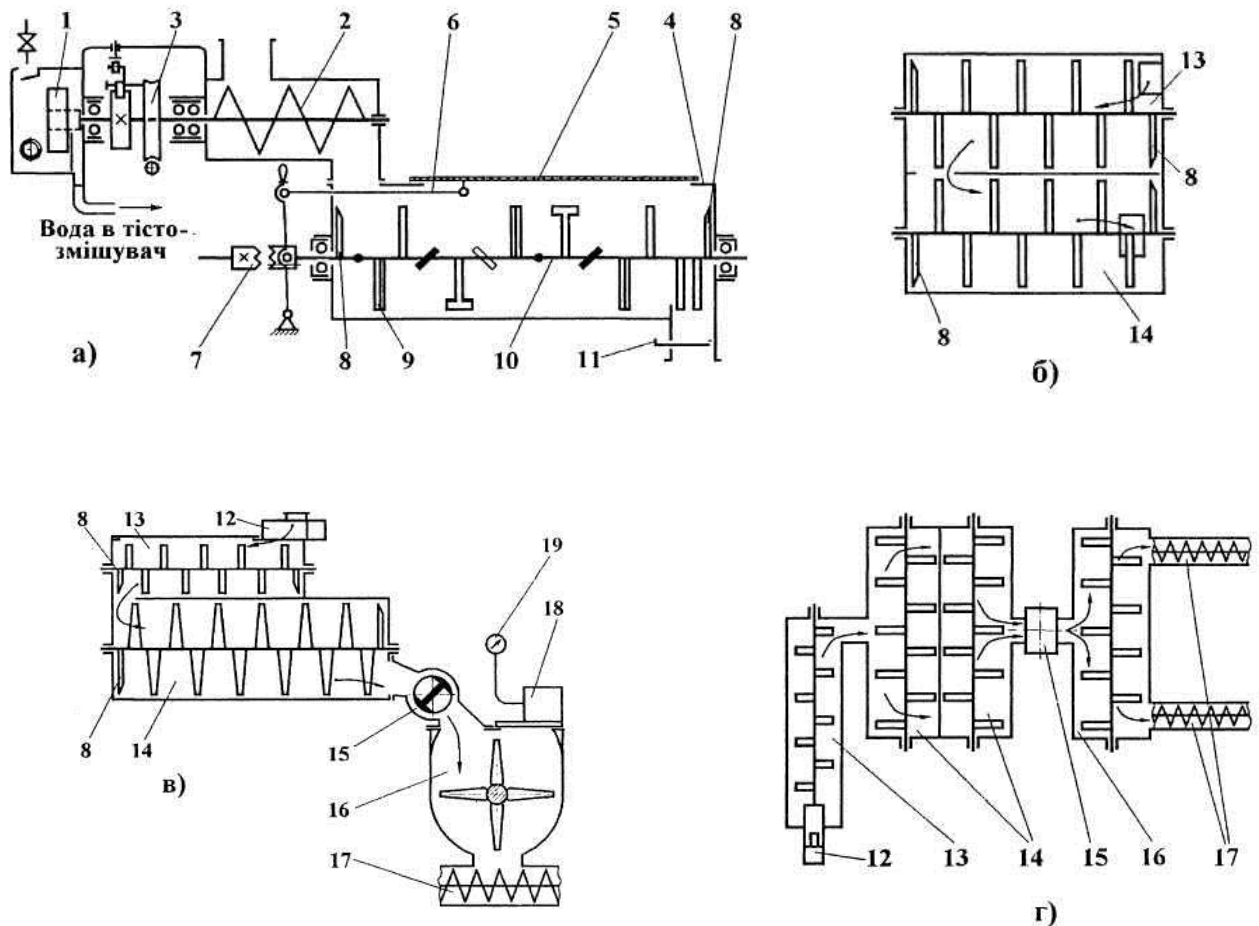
Схеми тістомісильних машин преса: а - однокамерної; б – двокамерної; в - трикамерної; г - чотирикамерної; 1 - черпакове колесо, 2 – дозувальний шнек; 3 - приводний механізм дозатора; 4 - корито тістомісильної машини; 5 - кришка корита, 6 - важелі блокування; 7 - кулачкова муфта; 8 - ножі для зачищення стінок корита; 9 - лопаті (стержні) місильного ротора; 10 - вал місильного ротора; 11 - засувка; 12 - дозатор борошна і води; 13 - камера попереднього змішування; 14 - камера кінцевого змішування; 15 - шлюзовий затвор; 16 - вакуумна місильна камера; 17 - пресуючий шнек; 18 - повітряний фільтр; 19 - вакууметр
